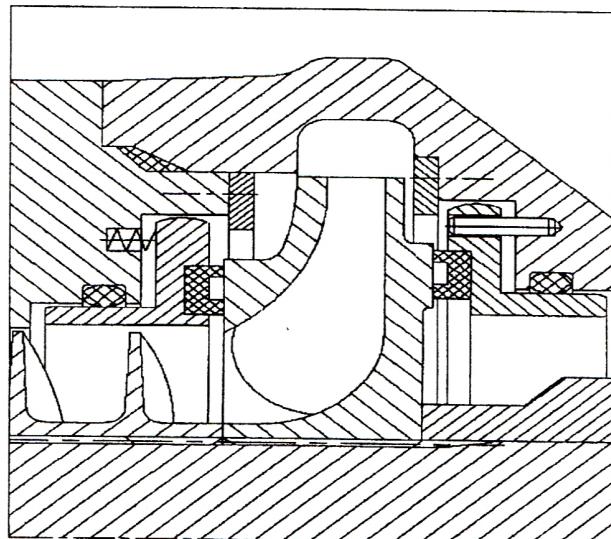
Установка торцовых уплотнений гидродинамического типа
